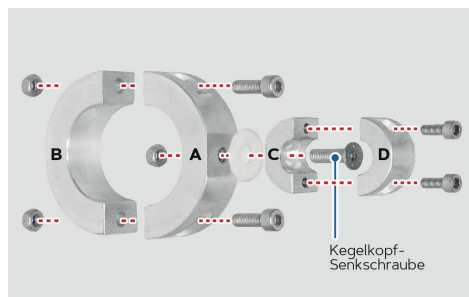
Klemmringkomplex für Befestigung der Chemiepestole
